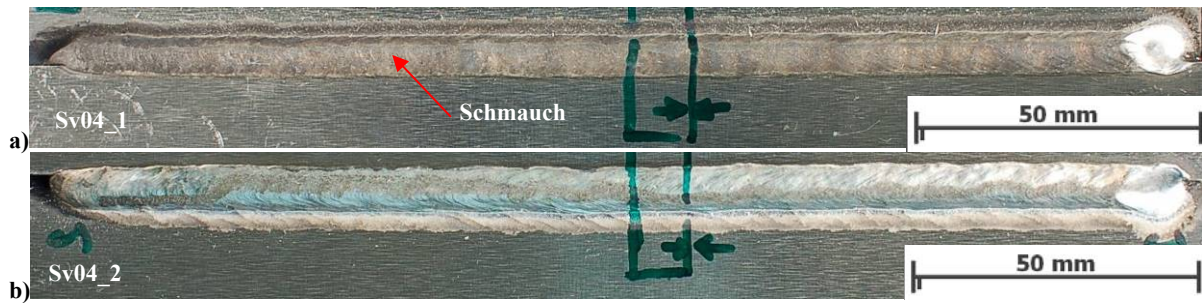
Einfluss des Anstellwinkels auf die Schweißschmauch- Niederschlag beim Schweißen von gereinigten AW-5083-O/AlMg5 Schweißnähten a) 15° schleppend b) 5° stechend
